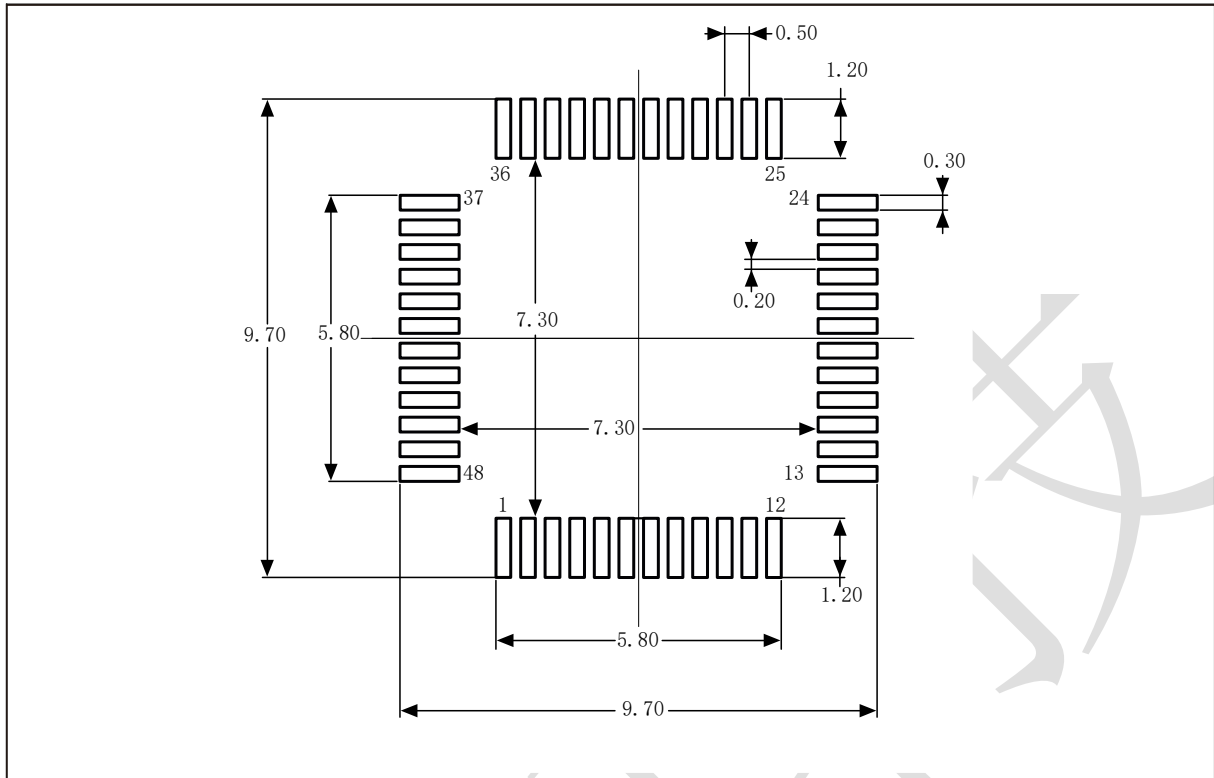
LQFP48 芯片的 PCB 安装尺寸图
